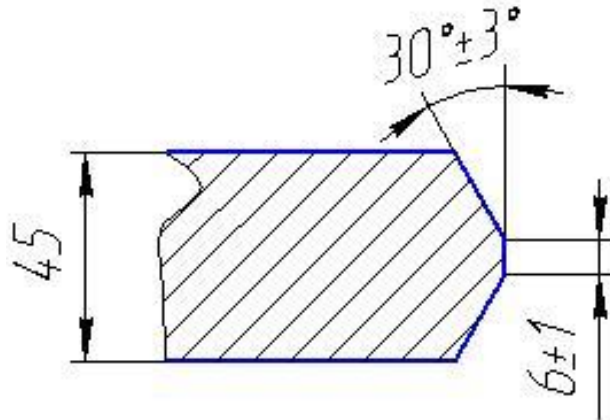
Ескіз оброблення кромки заготовки днища.
